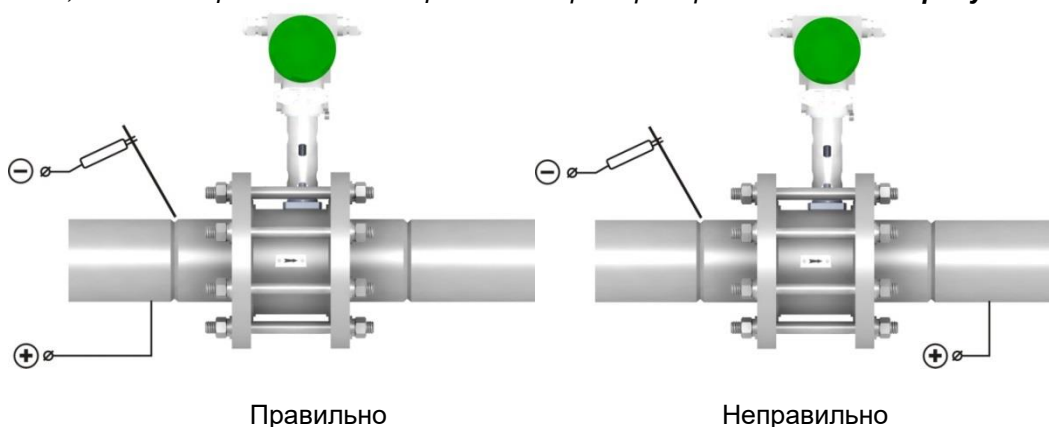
Подключение источника тока при электродуговой сварке
